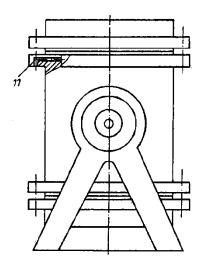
Устройство для электрогидравлической штамповки (вид сбоку)
